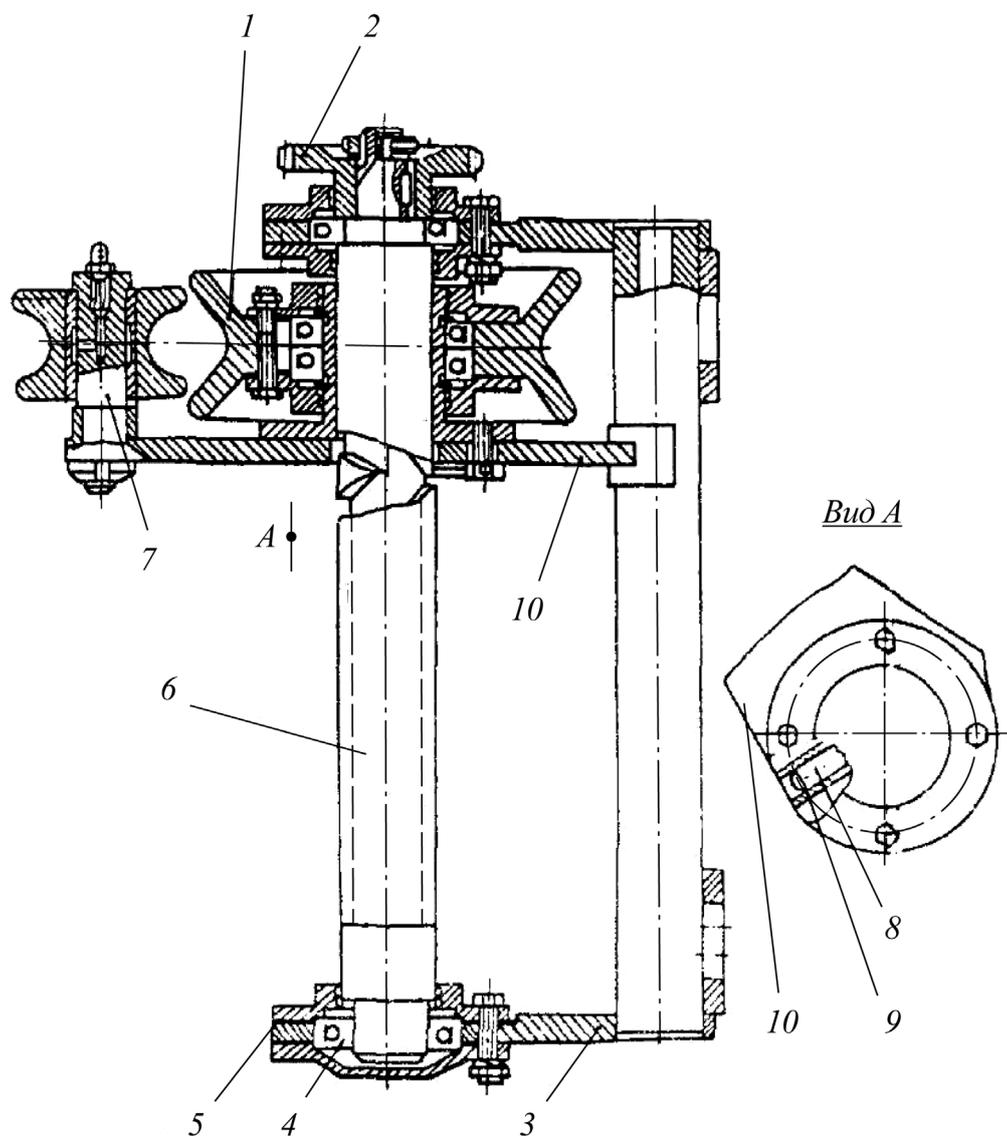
Кабелеукладчик: 1, 7 – ролики; 2 – звездочка; 3 – кронштейн; 4 – подшипник; 5 – крышка; 6 – вал кабелеукладчика; 8 – фиксатор; 9 – втулка фиксатора; 10 – стойка
